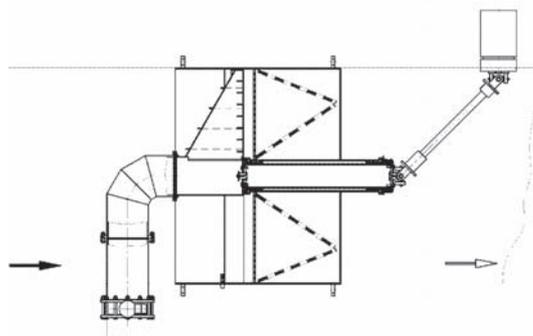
Монтажная схема и внешний вид фильтра типа ФСБ
